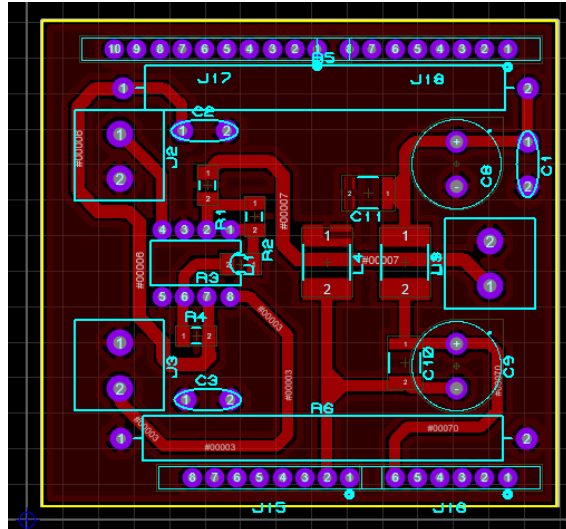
Diseño de pcb del circuito para medir voltaje.
